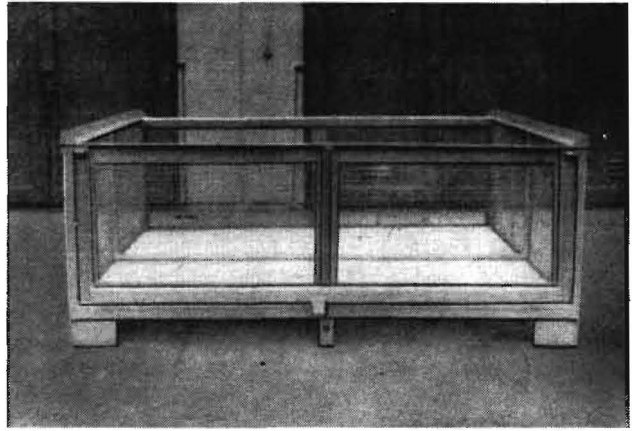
Der Großbehälter ist eine Stahlleichtbaukonstruktion mit Drahtverkleidung und Holzrostboden
